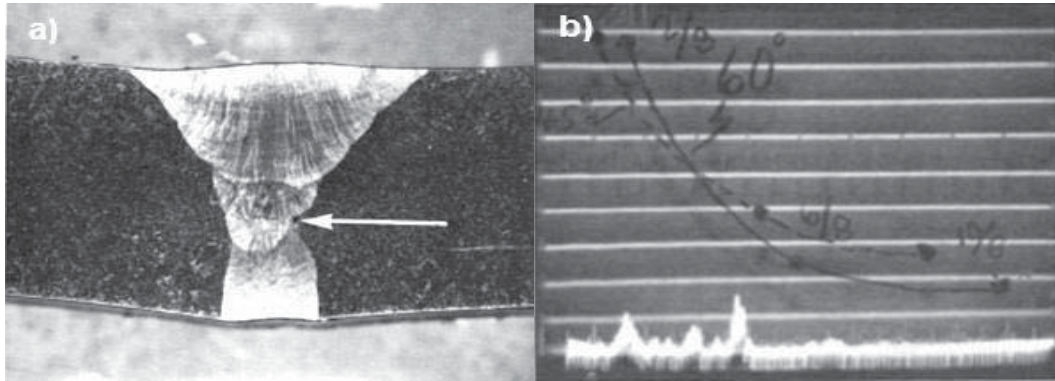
a) Macrografía que muestra un defecto dentro de la soldadura por fusión incompleta, b) señal A-Scan del defecto por fusión incompleta.
